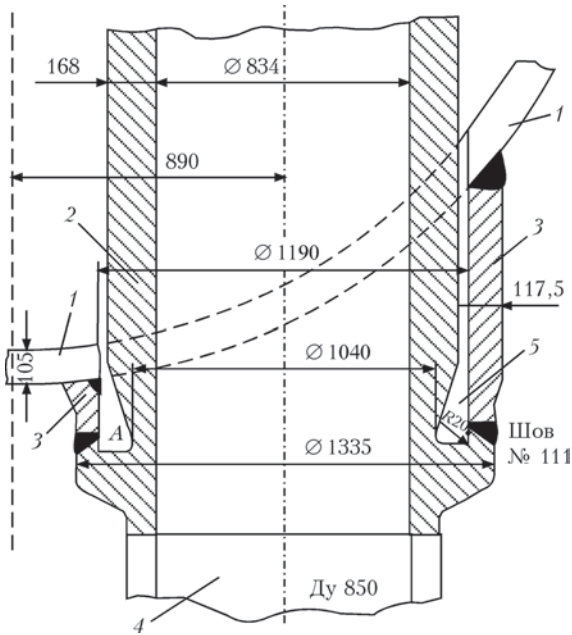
Схема вузла зварного з'єднання № 111: 1 — корпус ПГ; 2 — колектор; 3 — патрубок Ду1200; 4 — трубопровід Ду-850; 5 — карман
